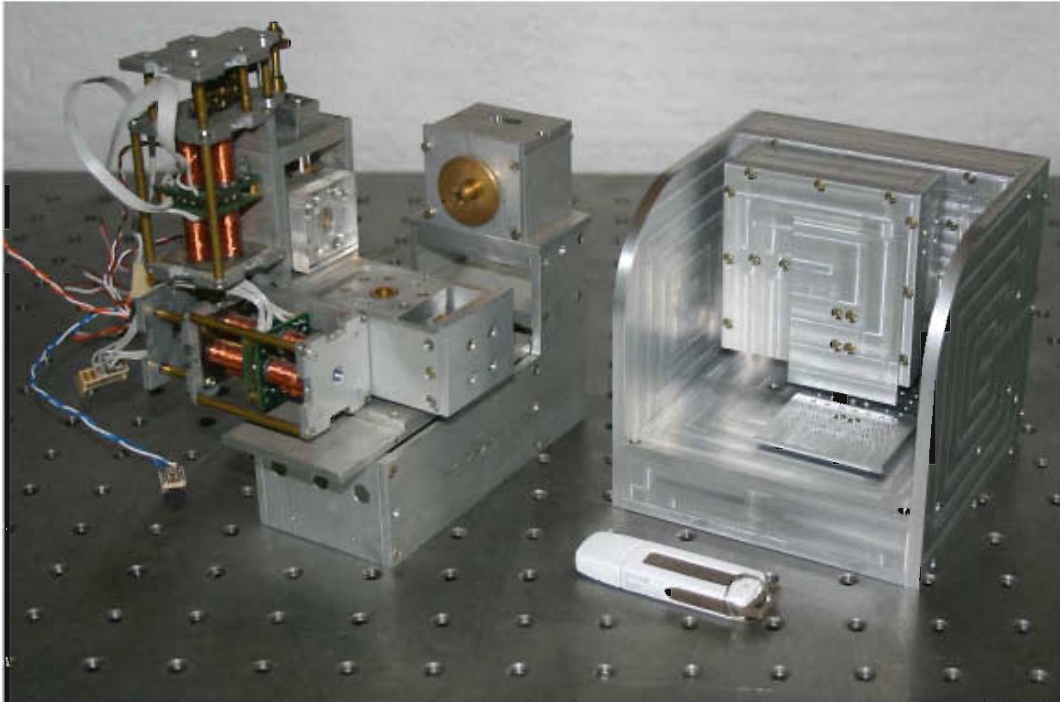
Nuevo prototipo de micromáquina herramienta desarrollada en el GMM.
